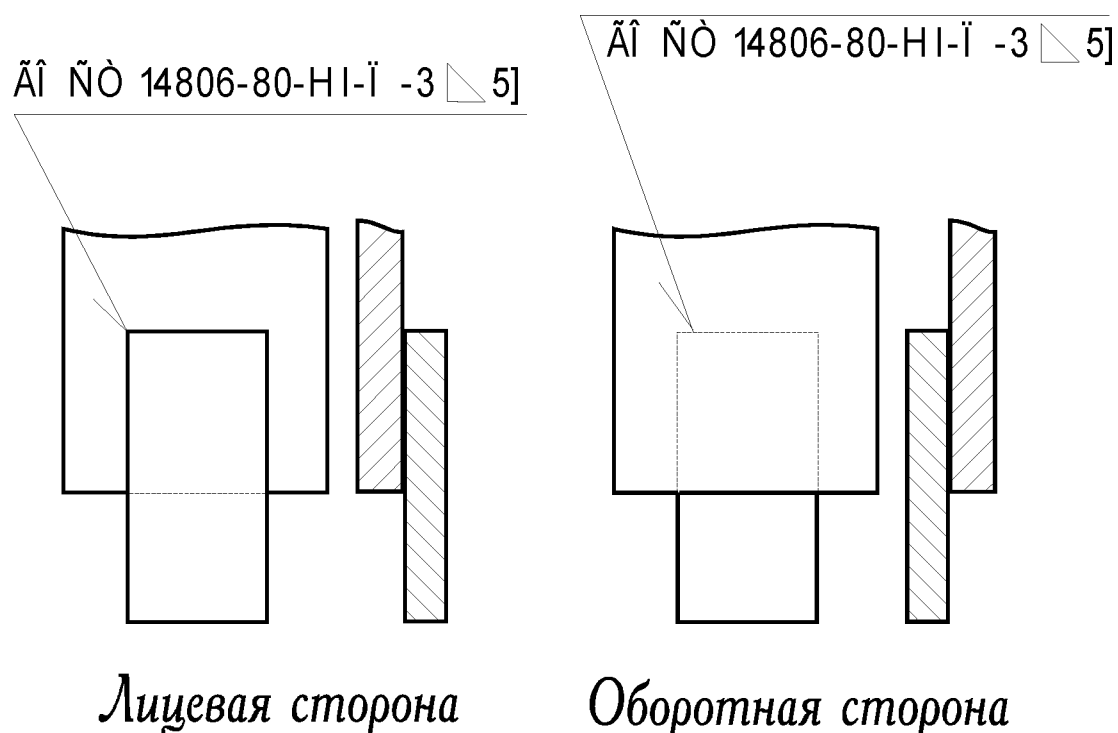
Примеры условного обозначения сварных швов на чертежах
